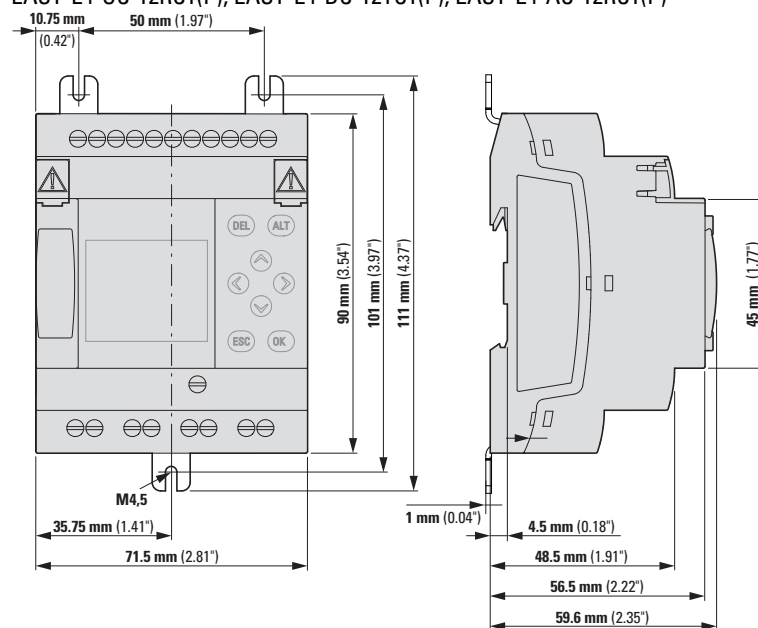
Dimensioni in mm (pollici) Apparecchi base EASY-E4-...-12...C1(P)
